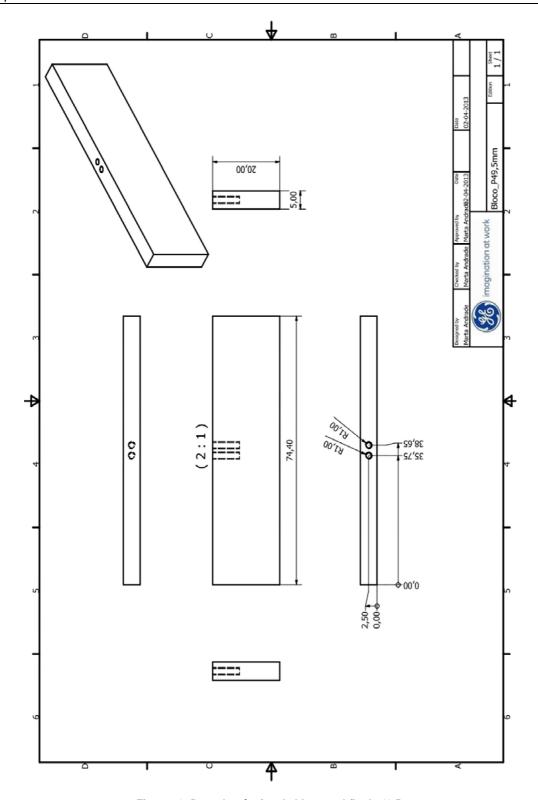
Desenho técnico do bloco padrão de 49,5mm
